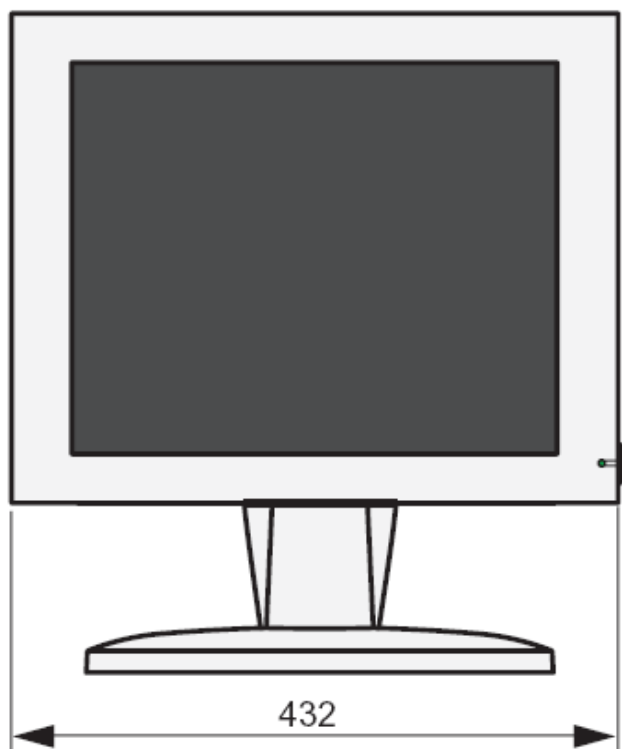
Dimensions extérieures (vue avant, format paysage)
